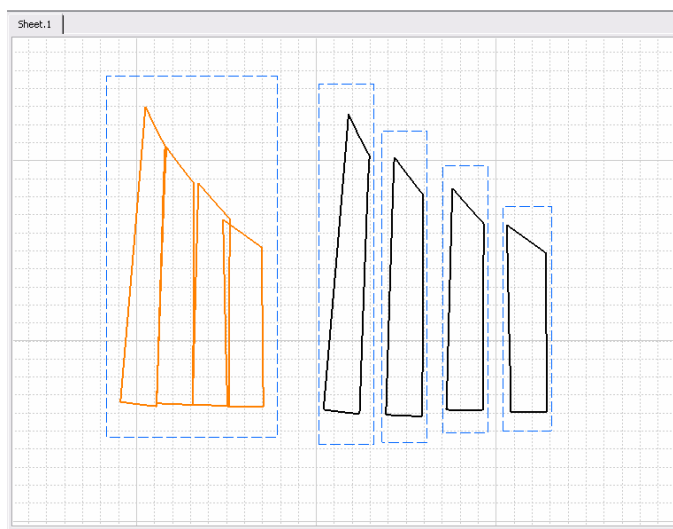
Vygenerovaná přední a zadní část torza figuríny v modulu Drafting
